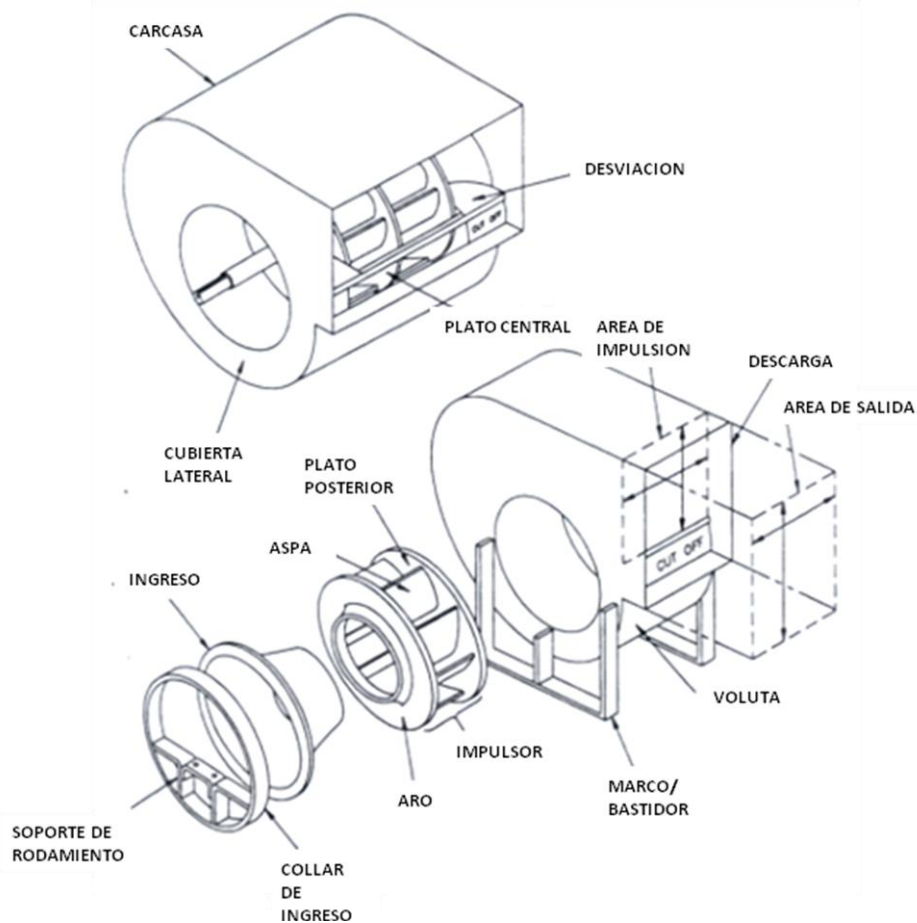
Ventilador Centrífugo (Montaje y Conjunto Armado)
